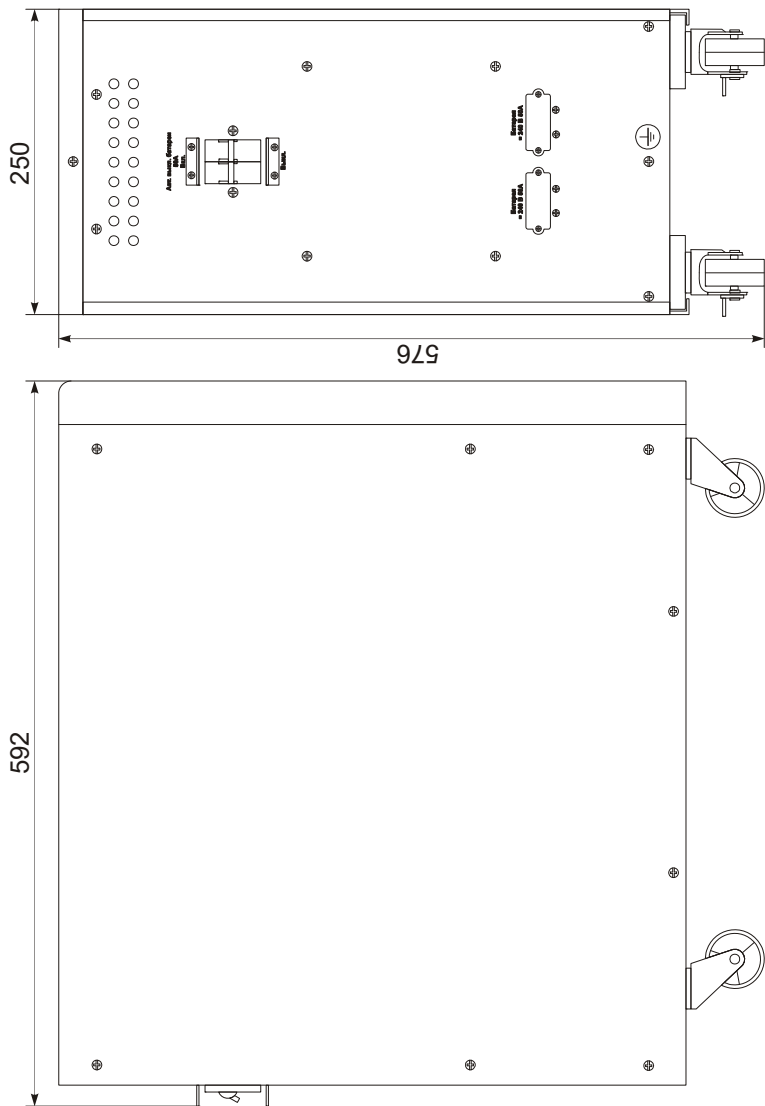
Габаритные и установочные размеры БМ ВР 240-18-50А
